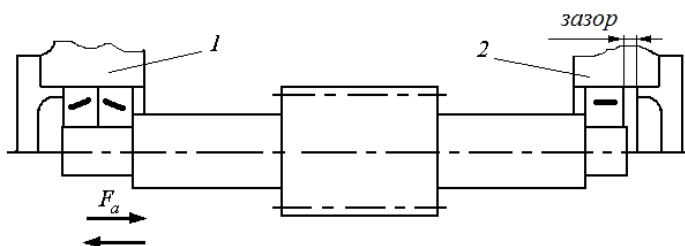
Установка червяка в опоры; опора 2 – плавающая
